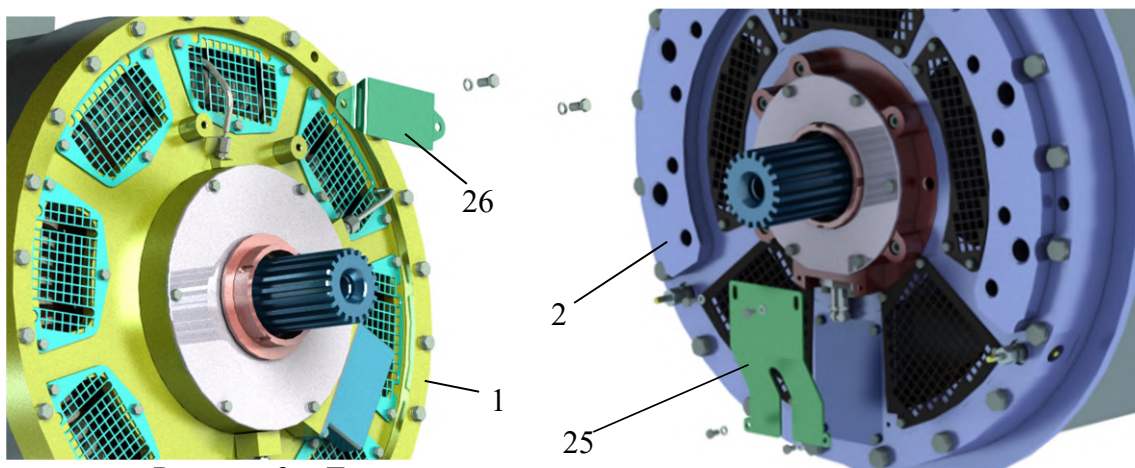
Демонтаж крышки датчика скорости и крышки датчика температуры подшипника
